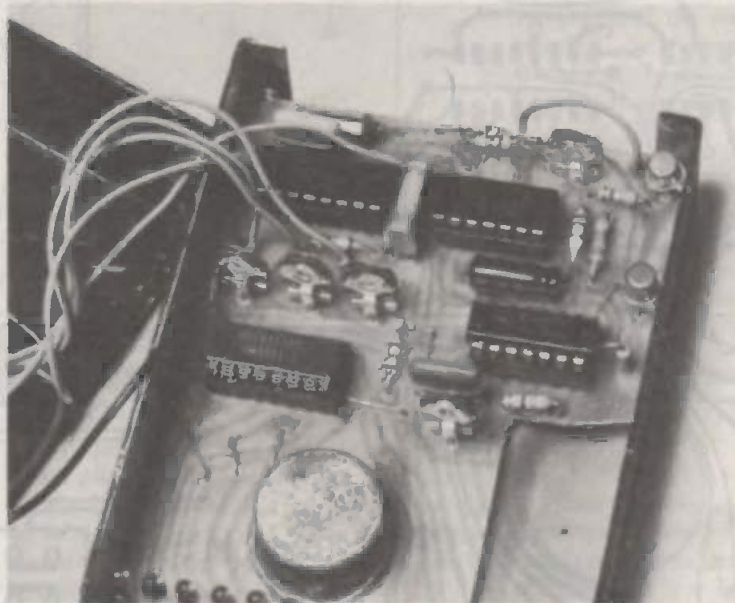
Il faudra prévoir une échancrure pour la place de la pile.
